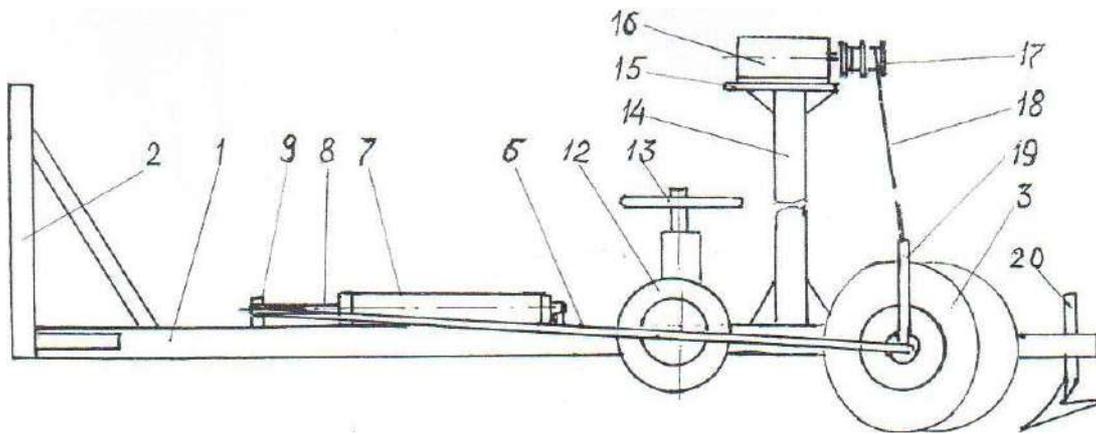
Почвообрабатывающая машина (вид сбоку):
